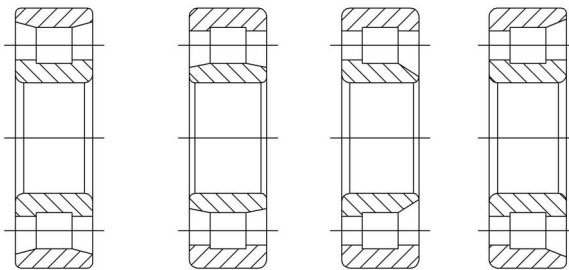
Роликові підшипники радіальні з короткими циліндричними роликами
